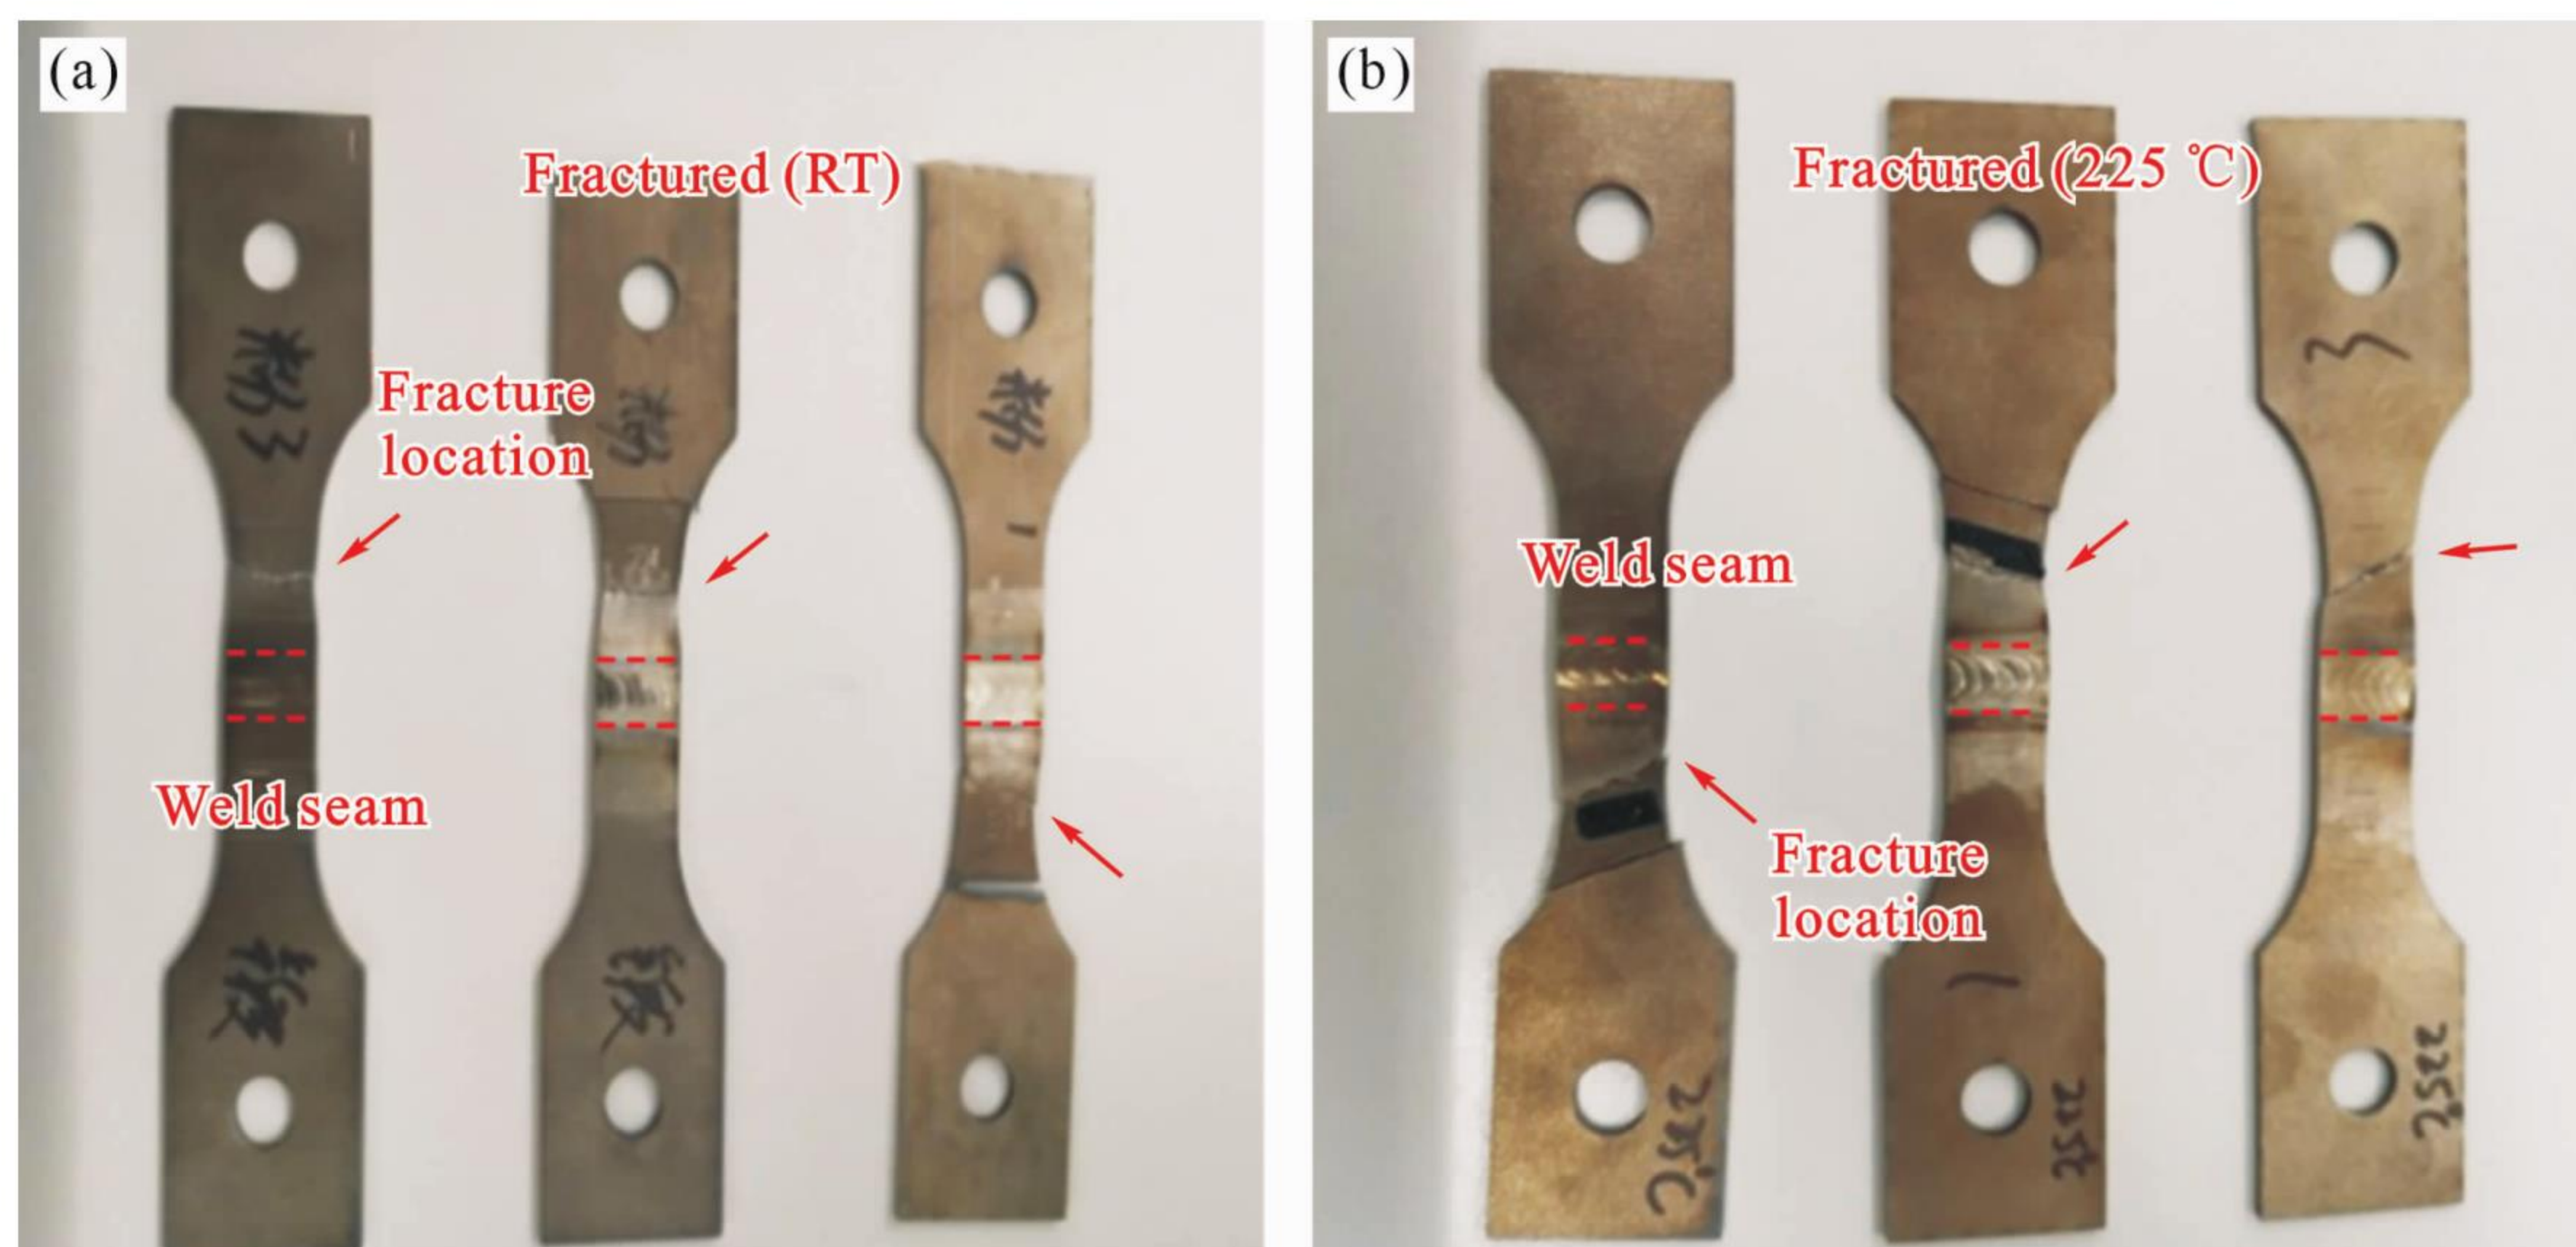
TA15 焊接接头拉断试样, 焊缝上半部分为粉末成形 TA15, 下半部分为锻造 TA15: (a) 室温拉伸断裂试样照片; (b) 225 °C 拉伸断裂试样照片
